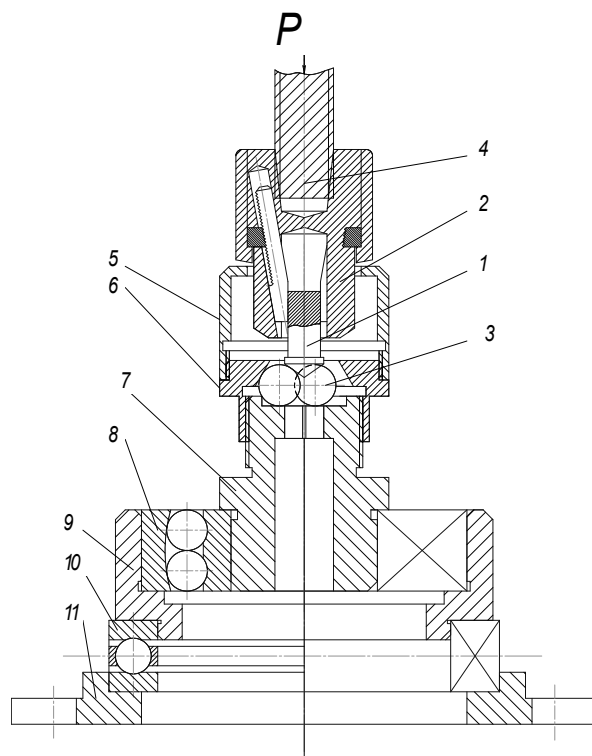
Робочий вузол установки для чотирикулькової схеми
